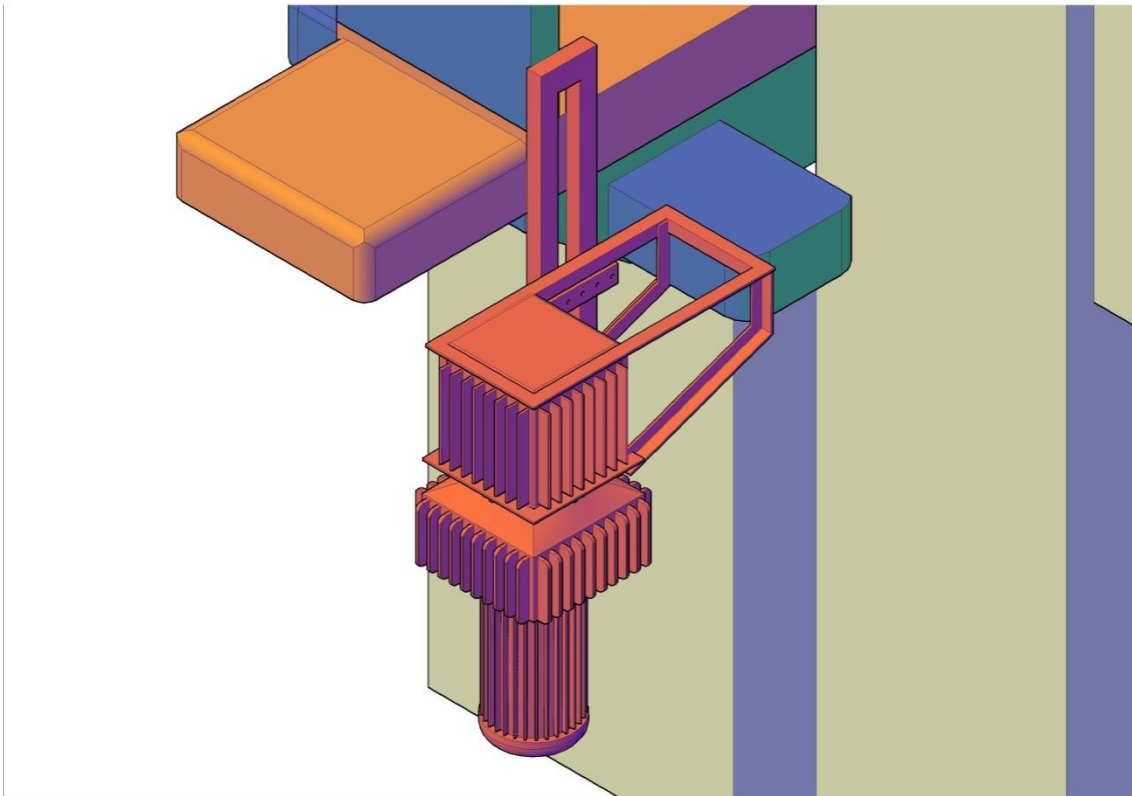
Montagem do motor e redutor para movimento longitudinal.
